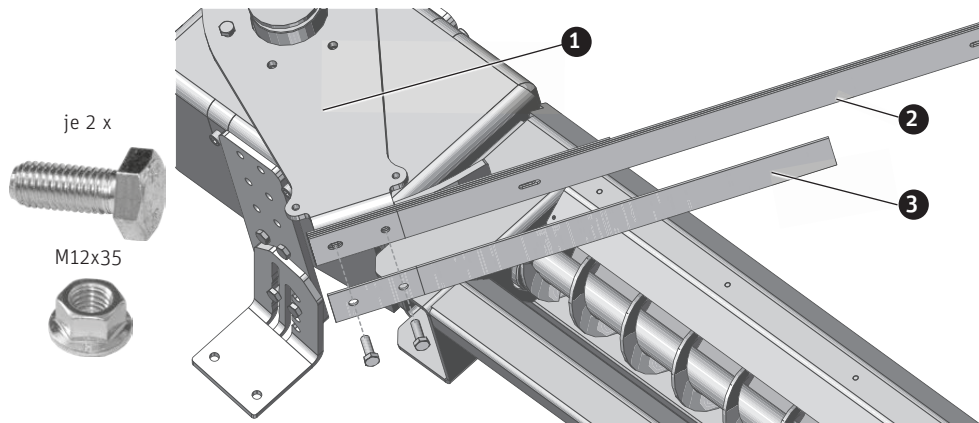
Blattfeder montieren, auf einer Seite außen die kurze Ausräumfeder mitschrauben
